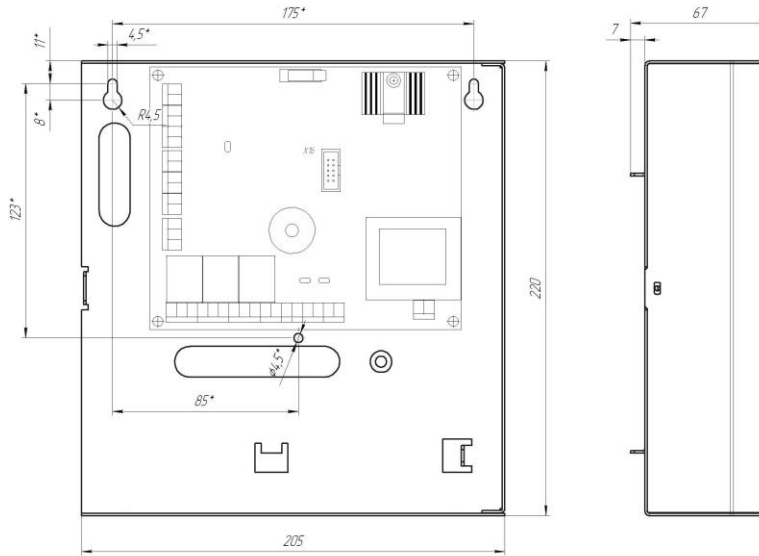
Габаритный чертеж и установочные размеры АПКП.
